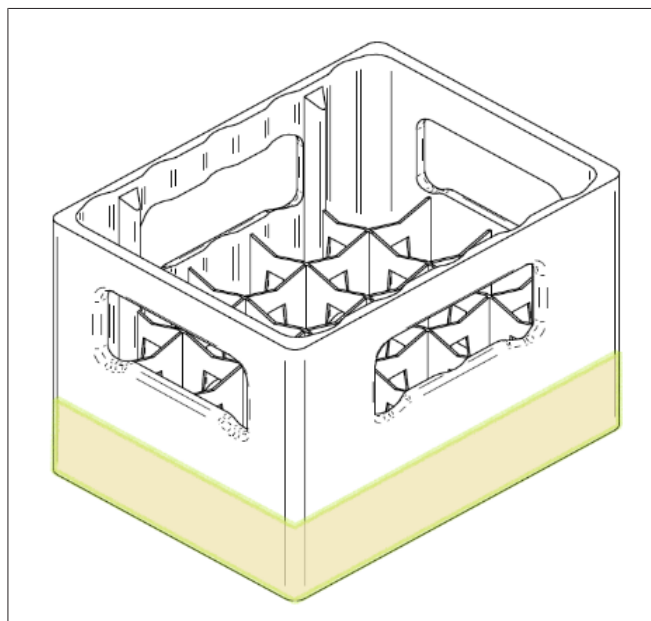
La zona più stabile si trova nella metà inferiore della cassa
